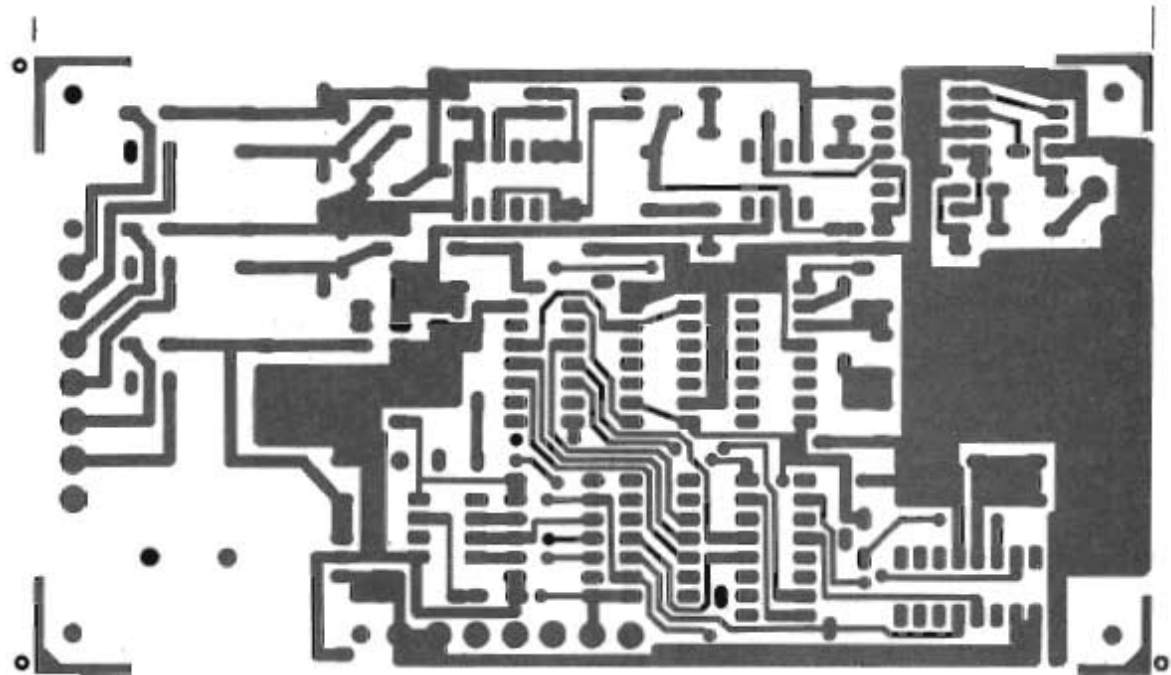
Master, lato saldature, in scala 1:1, del circuito stampato della basetta principale.
